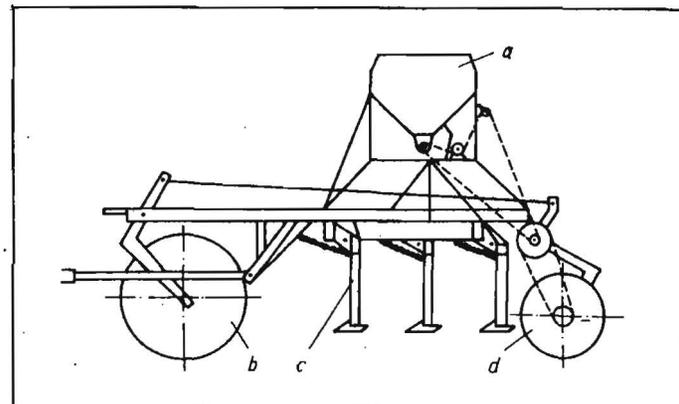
Grubberdrillmaschine SZS-2,1 mit Druckrollen; a Saatgutbehälter, b Stützrad, c Drillschar, d Druckrolle
